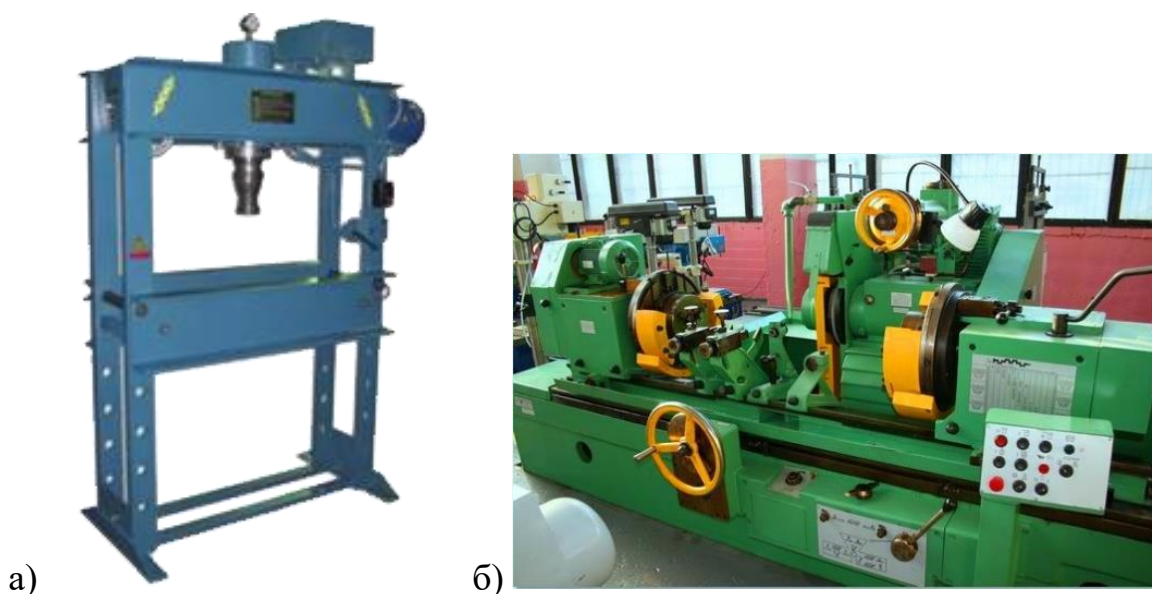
Гидравлический пресс для правки вала (а) и копировальношлифовальный станок (б)
